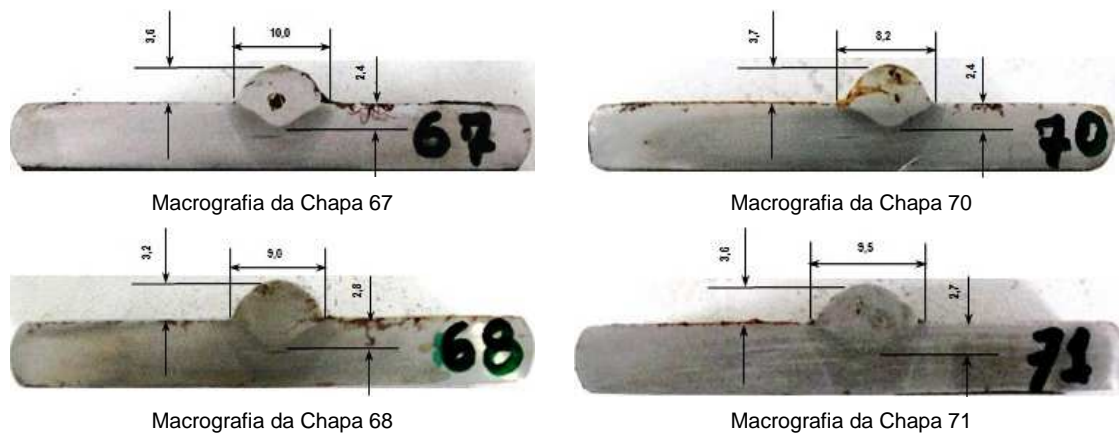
Macrografias com altura do reforço (r), largura do cordão de solda (b) e a penetração das soldas com Ar+8% H_2 .
